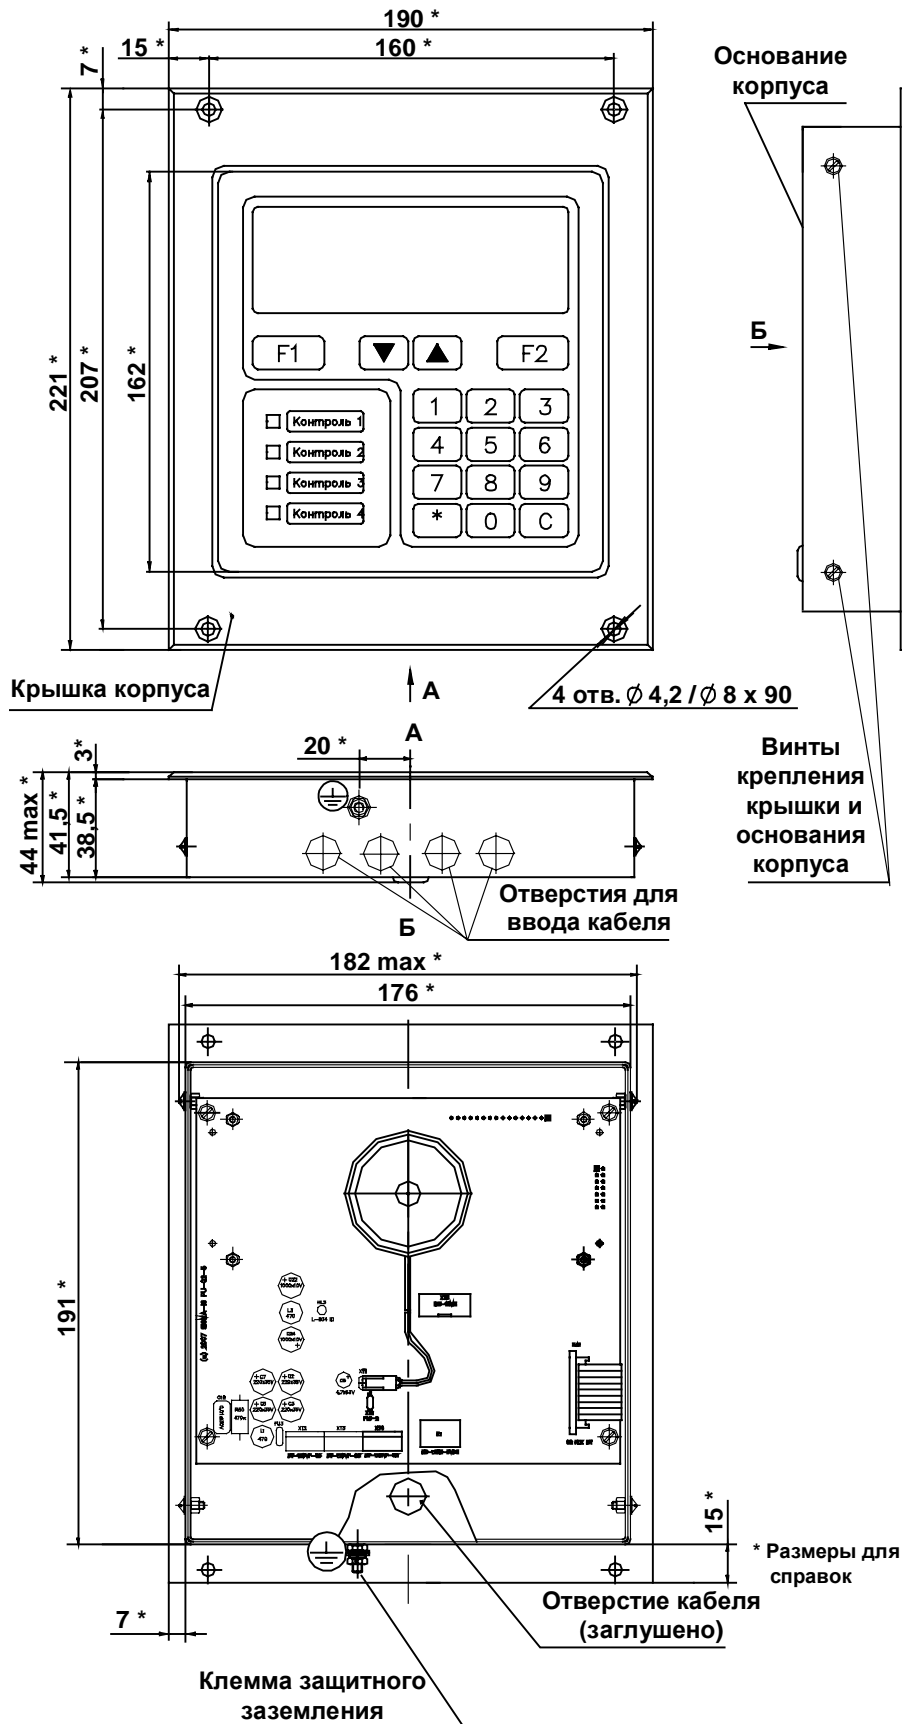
Габаритные и присоединительные размеры (врезное исполнение Тип 2)
